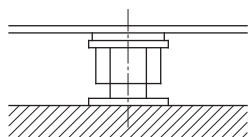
Нівелірні гвинти на поверхні фундаменту
